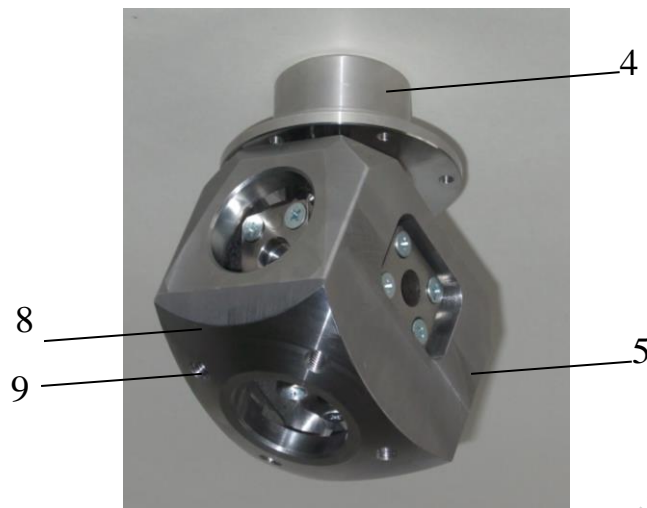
Корпус з отворами в які поміщаються втулки для закріплення керамічної кулі: 4 – кришка; 5 – корпус; 8 – сферична поверхня; 9 – різьбові отвори
